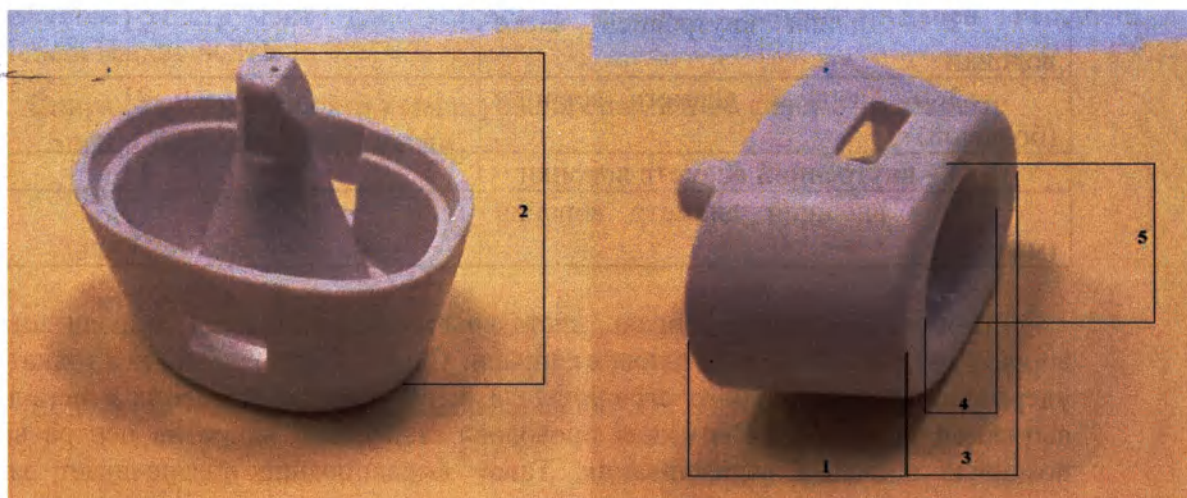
Внешний вид воронки Инструмента для установки спирали эмболизирующей Pod Penumbra Detachment Handle
